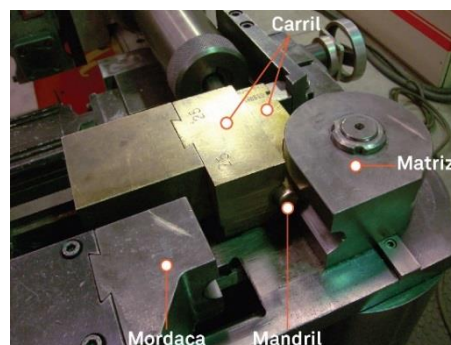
Disposição e designação da ferramenta de dobragem de tubo da máquina CNC.
